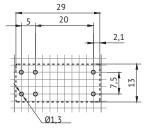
Установочные размеры для печатного монтажа для pene OptiRel G RP40-52 и OptiRel G RP40-61 с NO контактами
